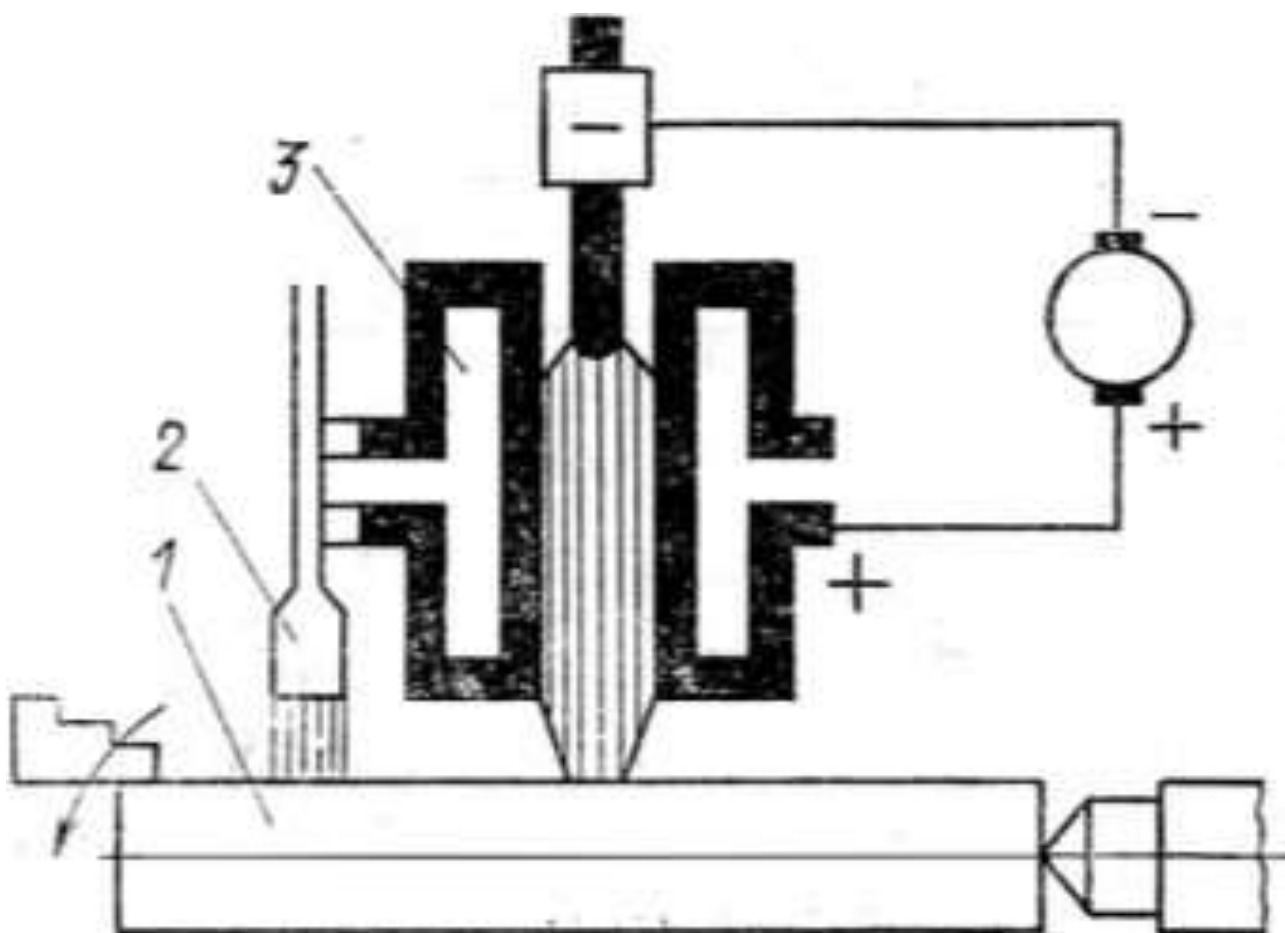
Схема установки для упрочнения ремонтируемых валов плазменным способом:
